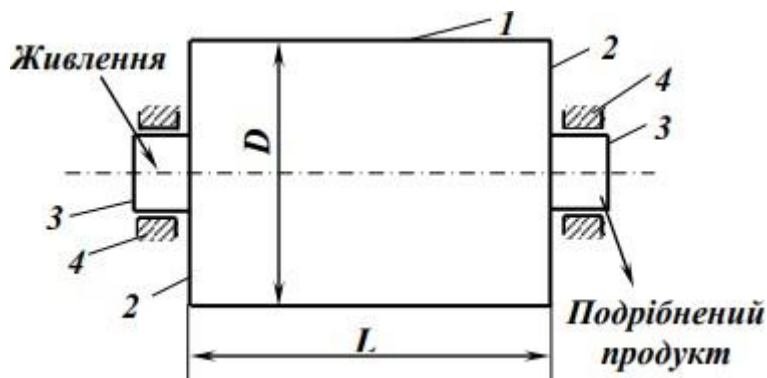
Схема барабанного млина. 1 – циліндричний барабан; 2 – торцеві кришки; 3 – цапфи; 4 – підшипники ковзання.
